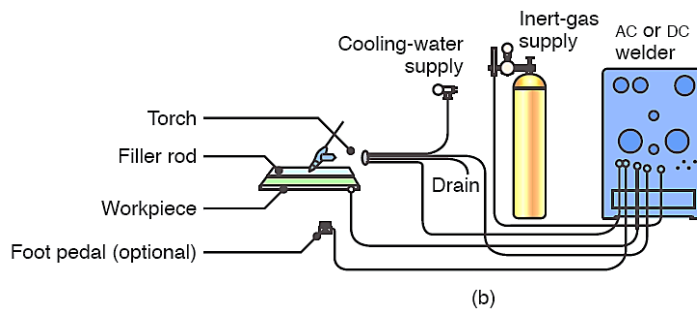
(a) Processo di saldatura TIG (*Tungsten Inert Gas*). (b) Equipaggiamento per le operazioni di saldatura GTAW. [13.b]
